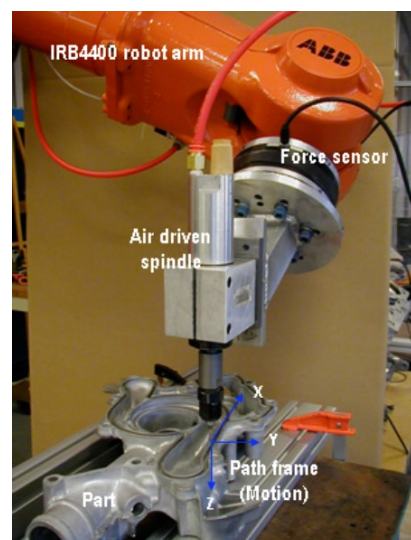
Фрезерование с использованием пневмопривода с базированием заготовки на столе [5]
